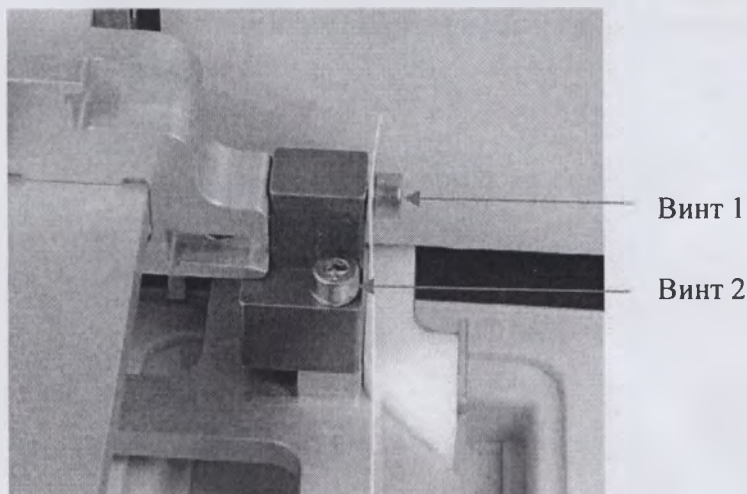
Транспортный фиксатор неподвижно закреплен
